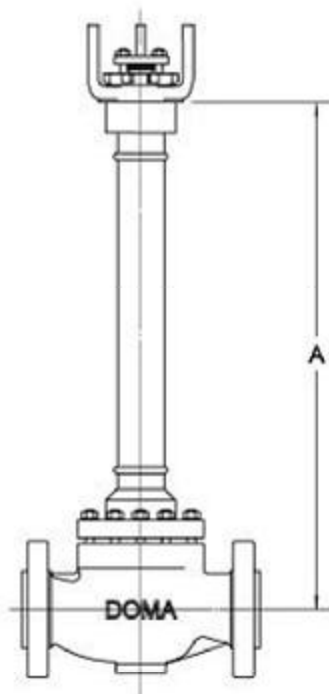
Bonete Extendido Soldado Estilo 3 (se debe indicar la cota "A")
